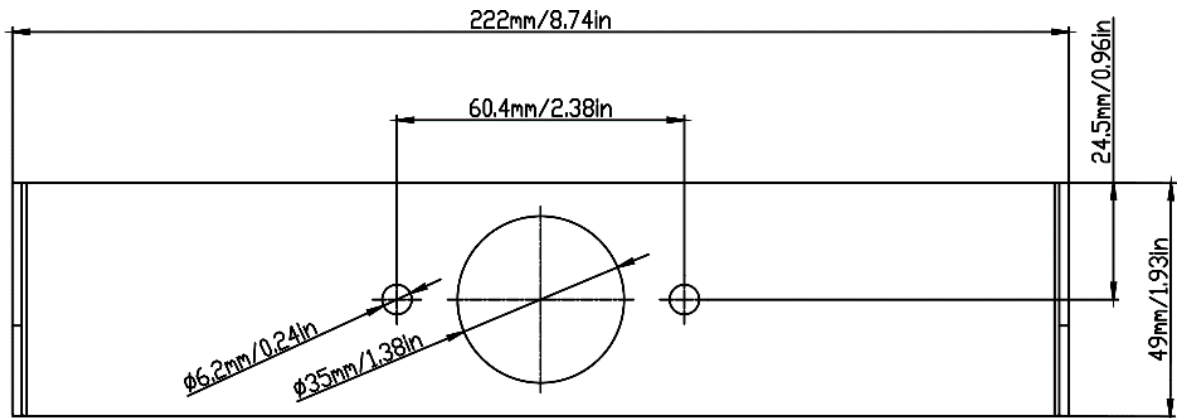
Dimensioni della staffa di montaggio i-DT33P
